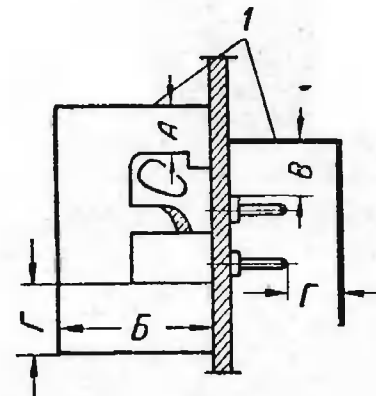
Расстояния при закрытии контакторов типа КП металлическими кожухами.
